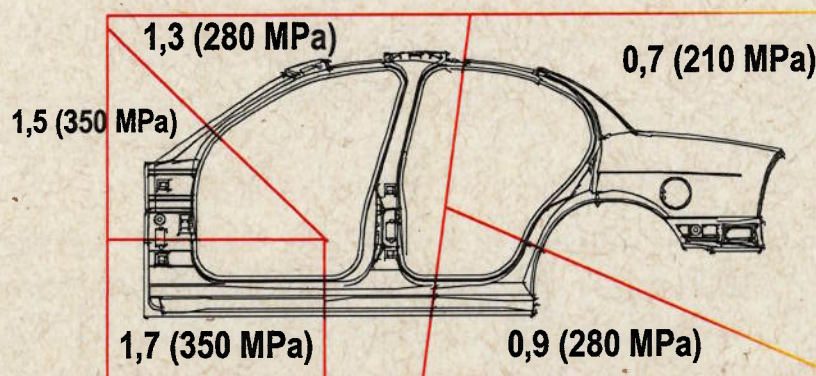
Painel lateral externo. - Obtido a partir da conformação de um "Tailor blank" soldado a Laser [Pereira99].
